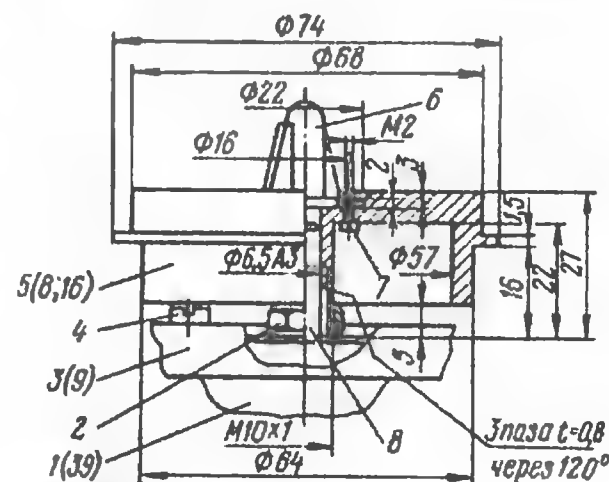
Приемный (подающий) узел: 1 (39) — электродвигатель АД-5У4; 2 — гайка специальная (от переменного резистора СП-11 или СП-111 со стопором оси); 3 (9) — шасси; 4 — винт М4Х6, 3 шт.; 5 (8, 16) — корпус подкатушника, Д16-Т; 6 — фиксатор катушки (от магнитофона «Яуза-206», доработать по чертежу, закрепить на дет. 5 винтами 7; 7 — винт М2Х4, 3 шт.; 8 — вал электродвигателя
